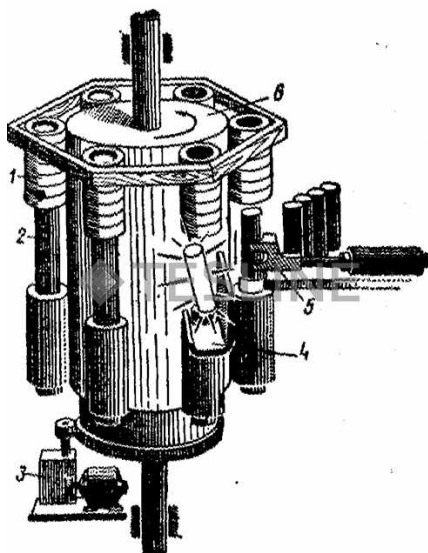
Схема карусельного нагревателя с шестью периодическими индукторами:
